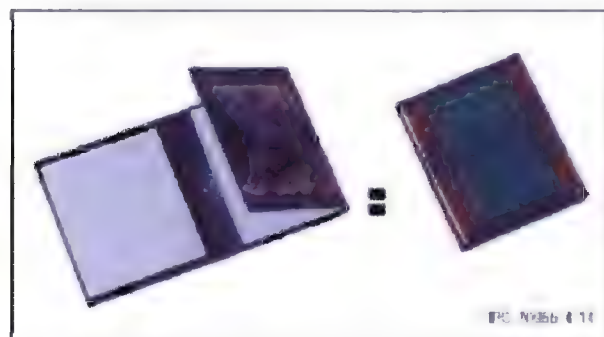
Корпус BGA с несколькими сложенными кристаллами
